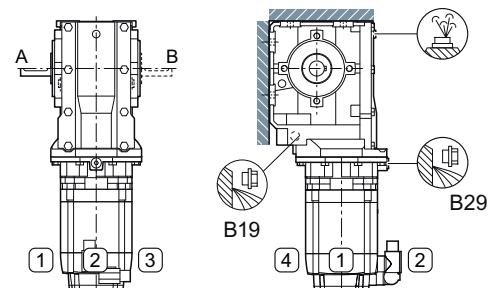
Einbaulagen für Servo-Flachgetriebemotoren FZAD und FDAD, Aufsteckausführung, Baugrößen 39 - 129, 2-stufig und 3-stufig
